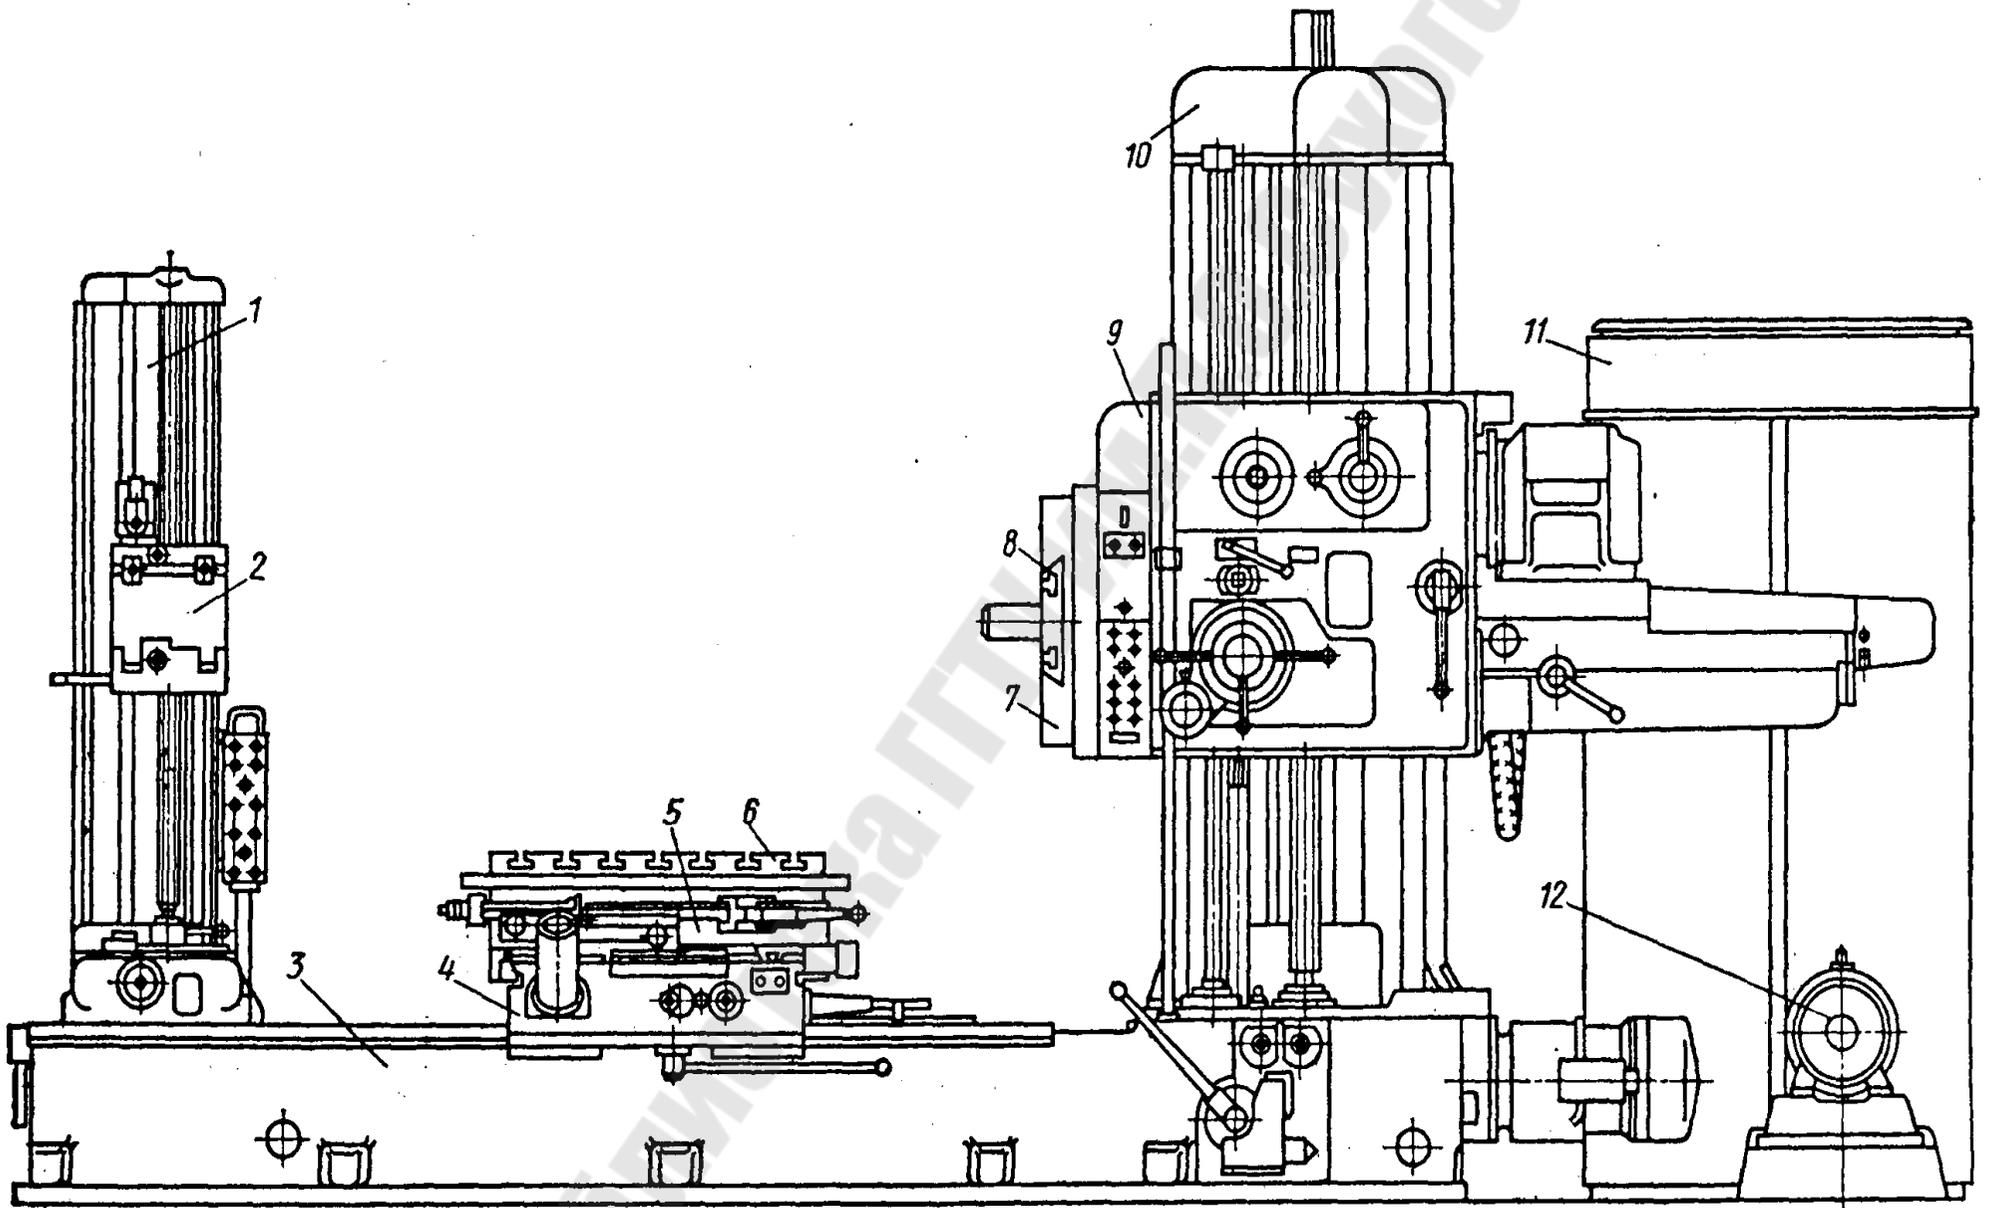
Общий вид горизонтально-расточного станка
